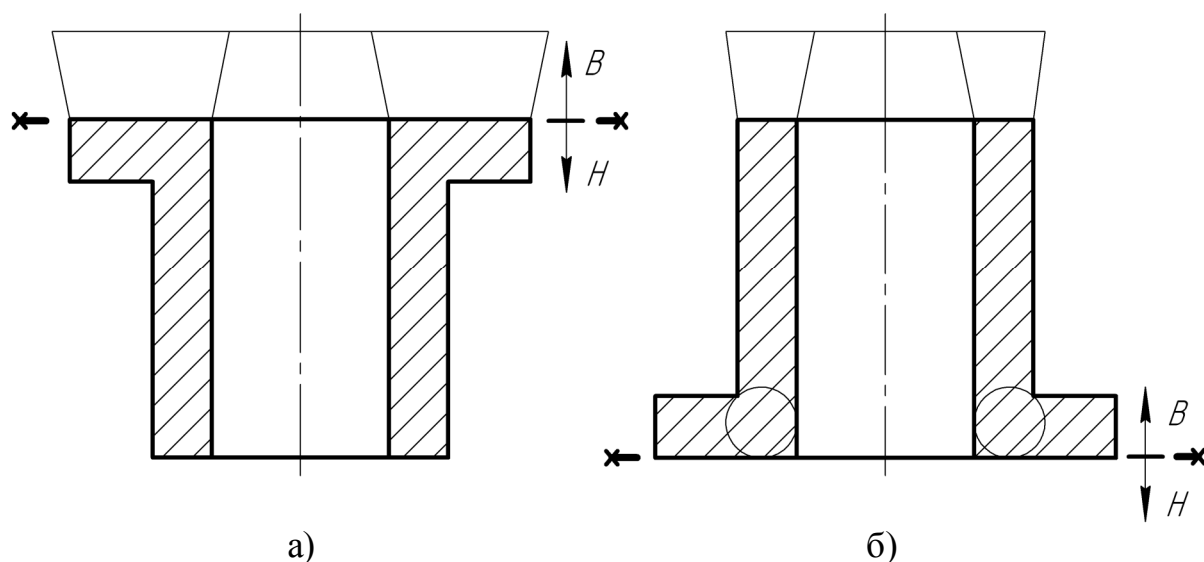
Выбор положения в форме отливки «Корпус люка»: а – правильный; б – неправильный
